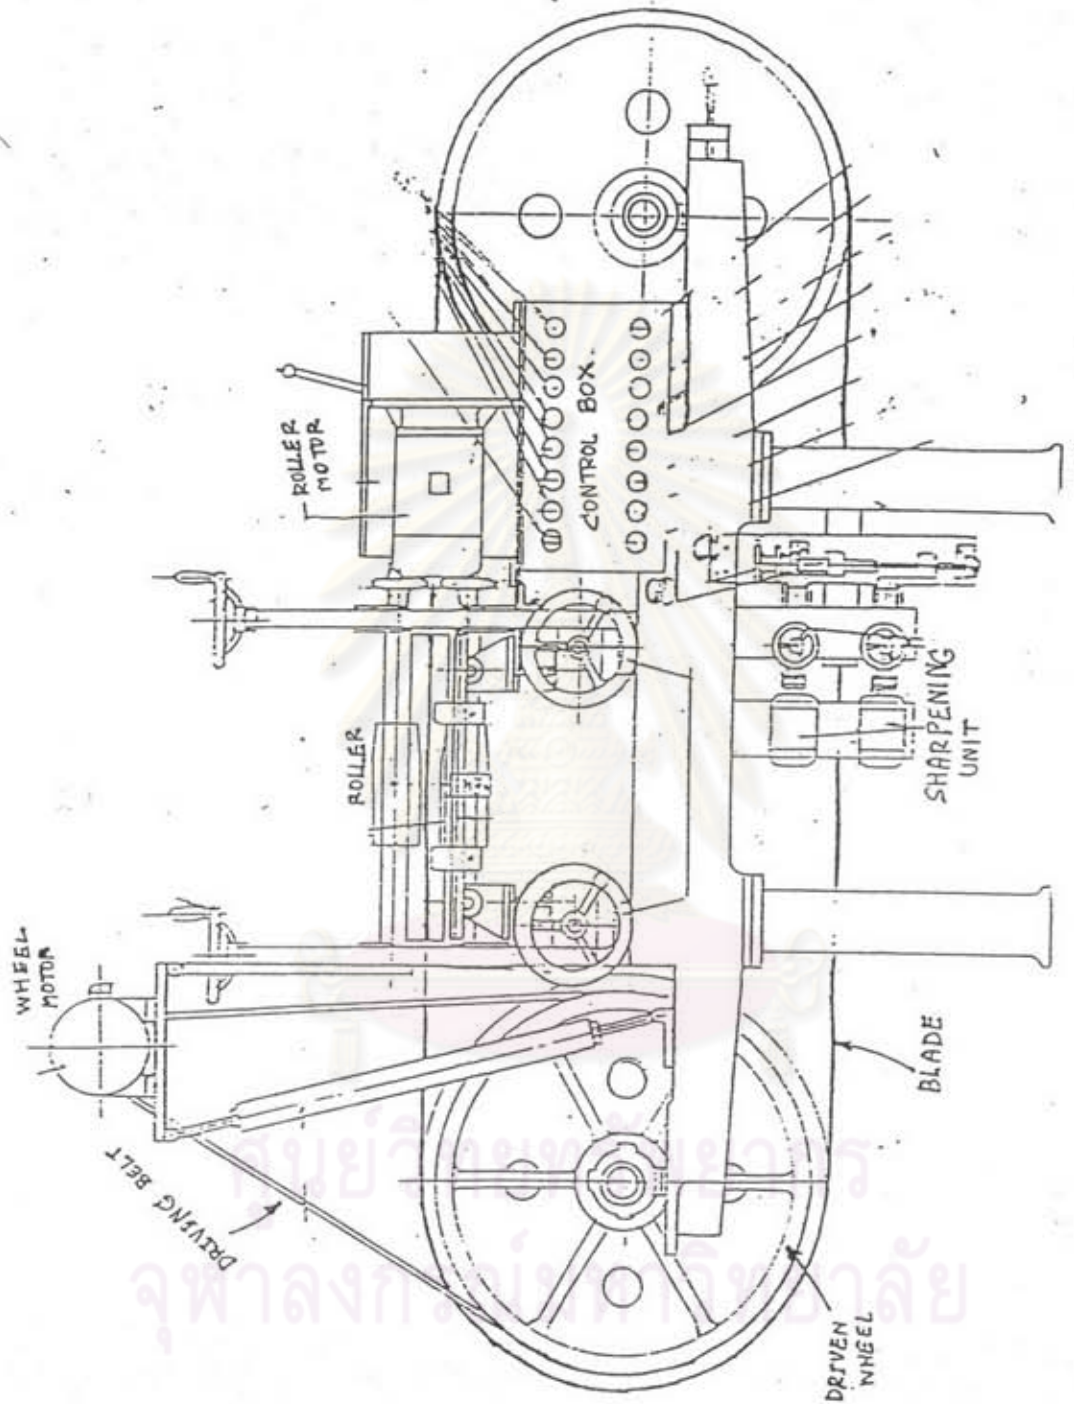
เครื่องตัดขอบ (Strip Cutting Machine)
